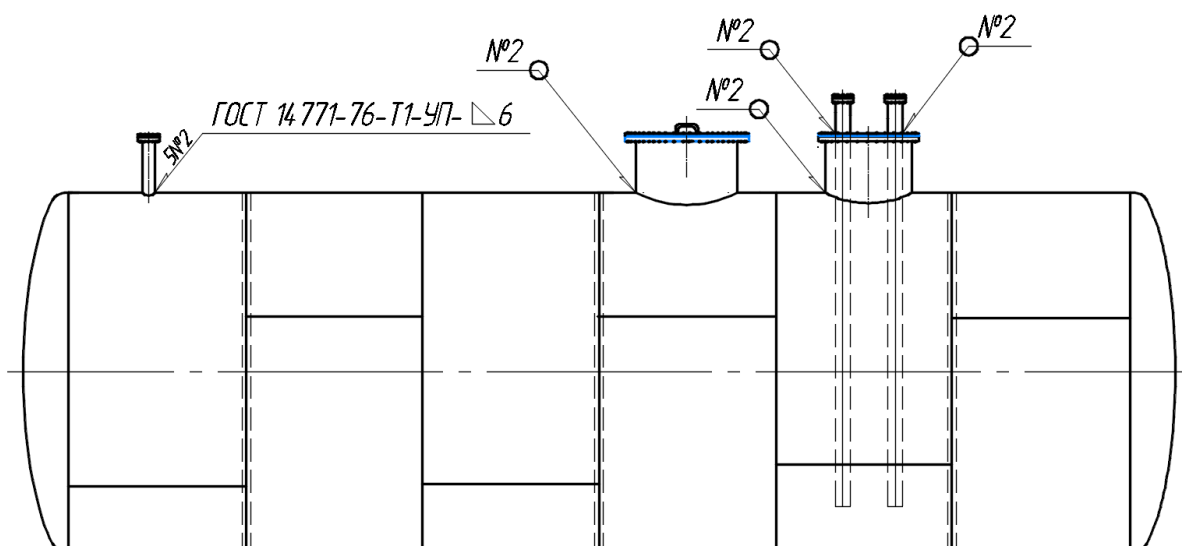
Сварка люка, горловины, патрубка
